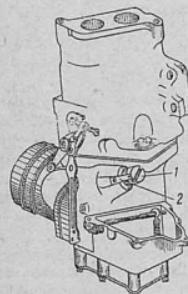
Регулировка карбюратора ЗИС-101 на холостые обороты
